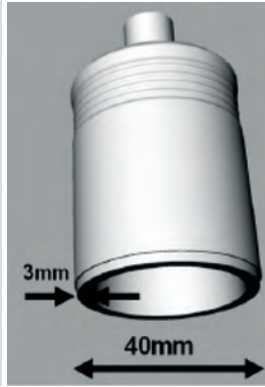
Fügen eines PP-Probekörpers mittel Zirkularschweißen
